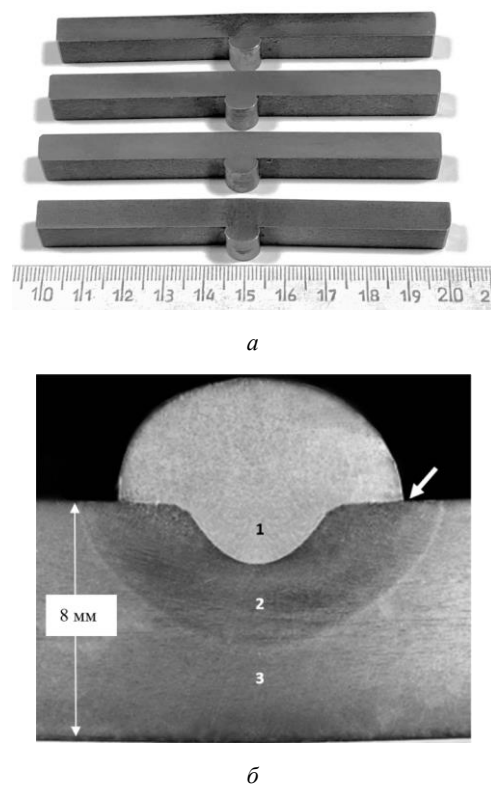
Образцы наплавленного металла на пластину (а) и макроструктура зоны наплавки (б): 1 – наплавленный металл; 2 – ЗТВ; 3 – основной материал
